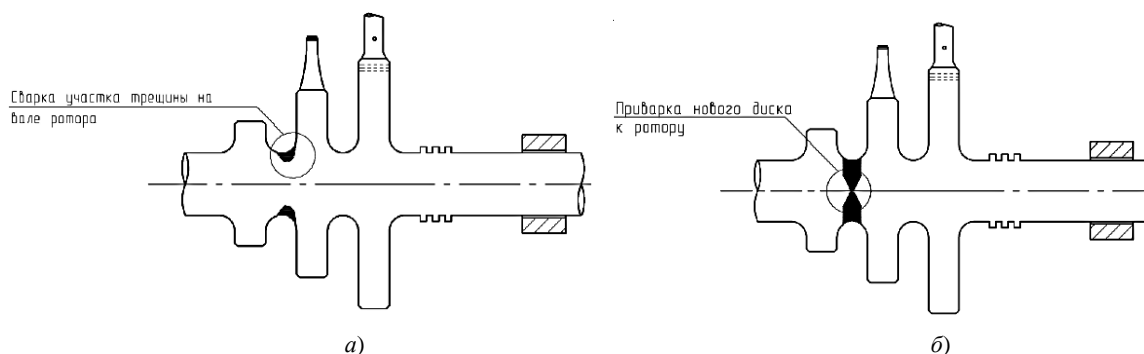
а — заварка участка трещины на вале ротора; б — приварка нового диска к ротору
